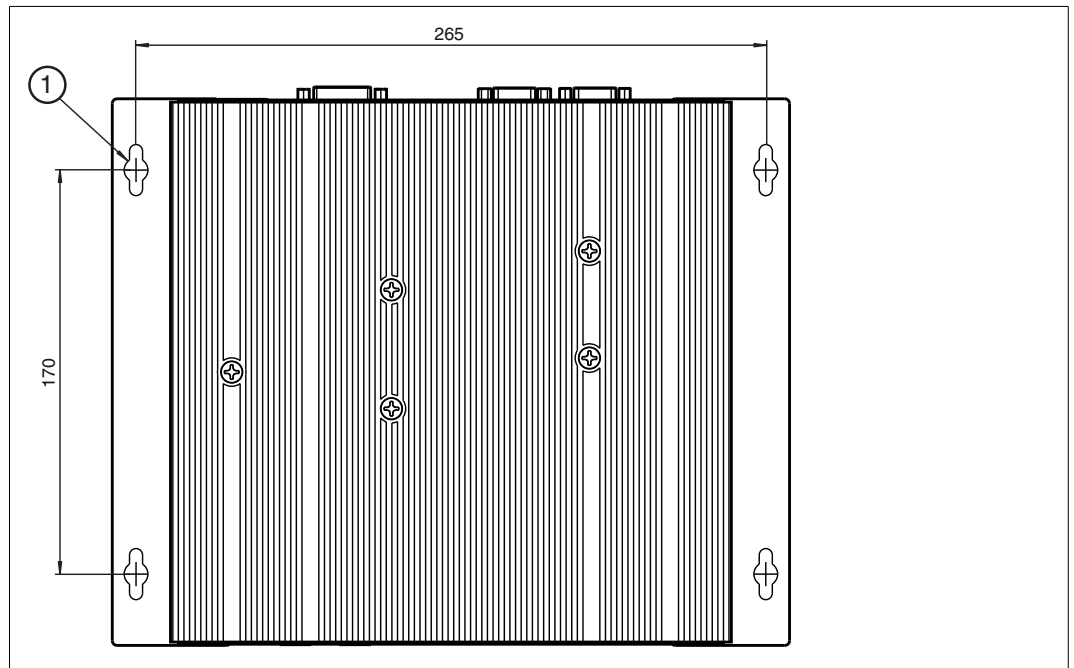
① – für Befestigungsschrauben mit 5 mm Durchmesser
